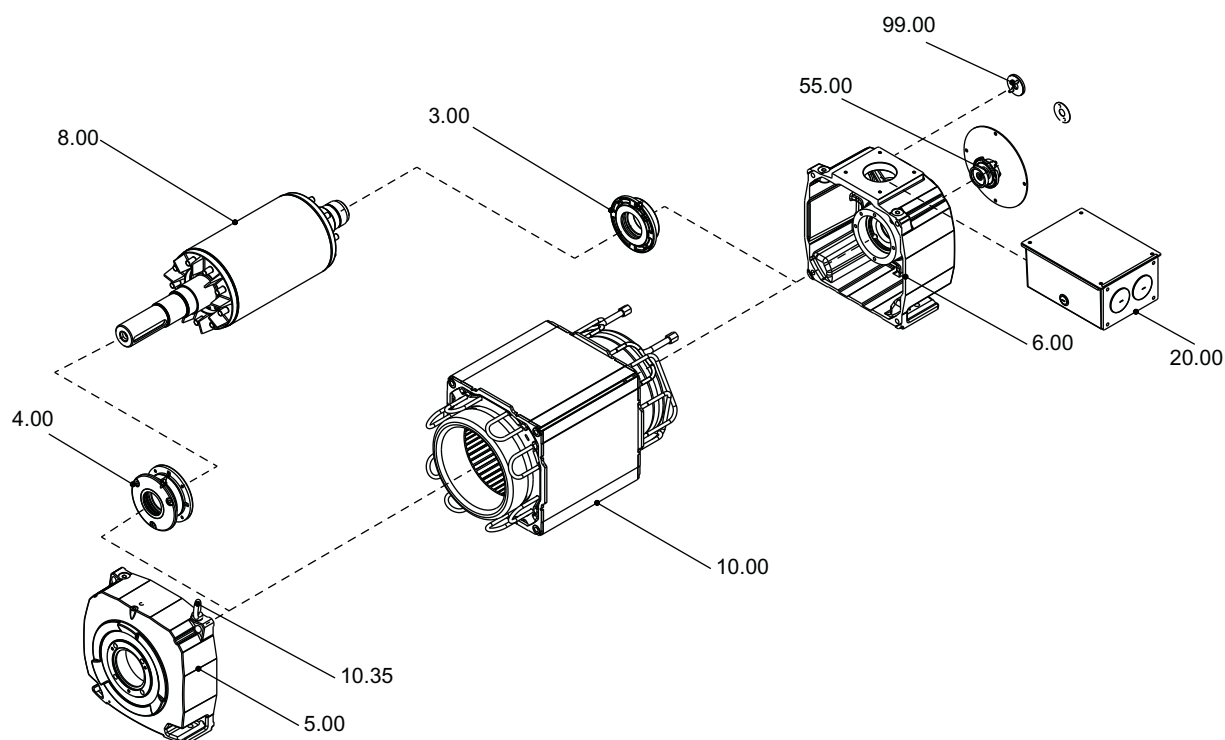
Принципиальный чертеж Мотор в сборе
